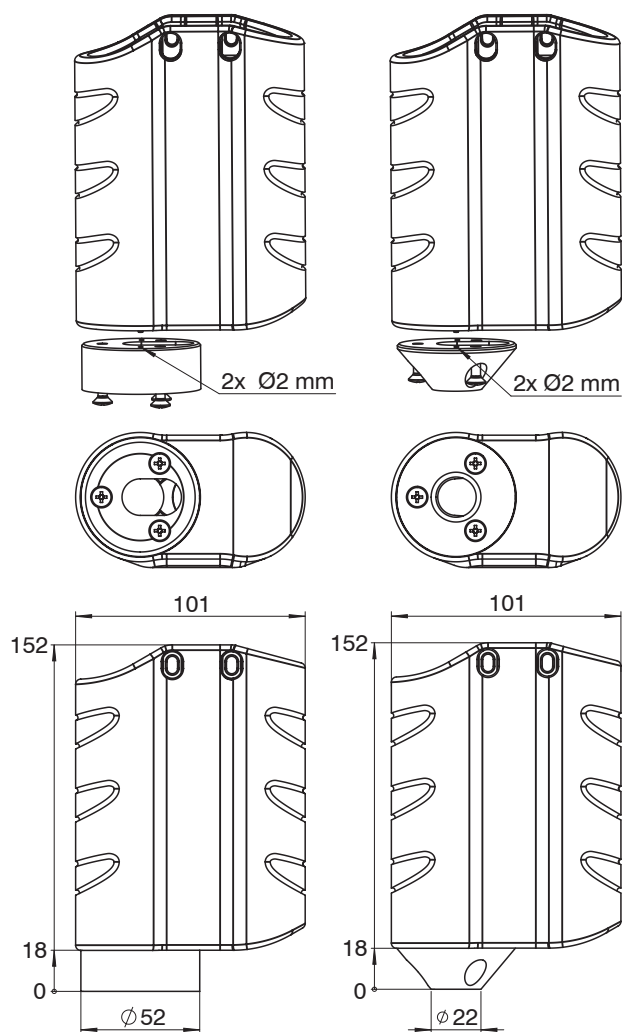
Adapter für Winkelsensor FCS-X-ACS1-30/0-50-XXXX
